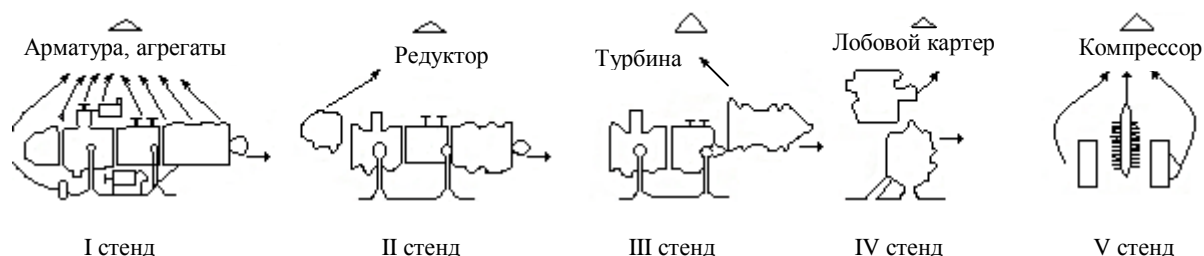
Схема поточной линии разборки авиадвигателя
